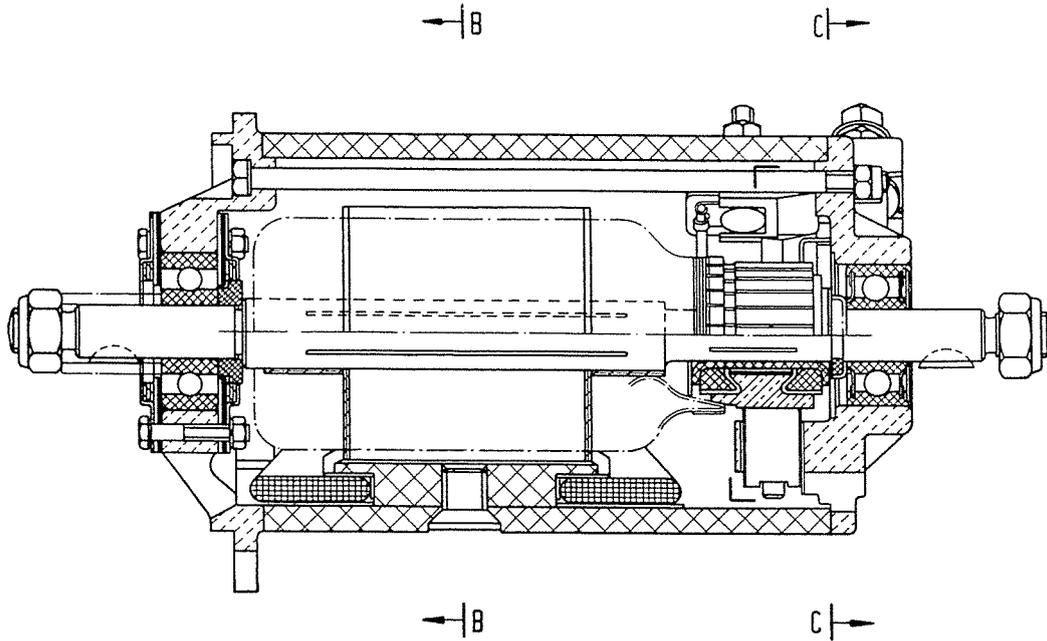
Längsschnitt durch die Lichtmaschine.
